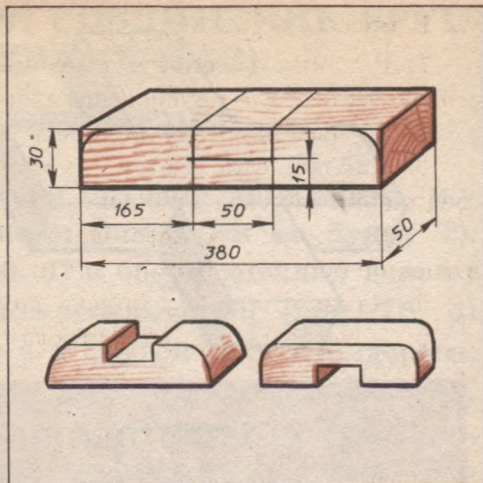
Размеченная заготовка и готовые детали для подставки.
